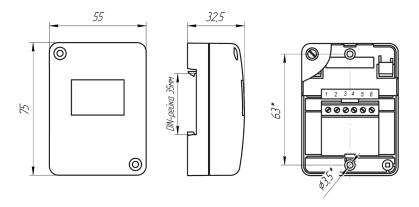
Габаритные и установочные размеры модуля МШ-1.
